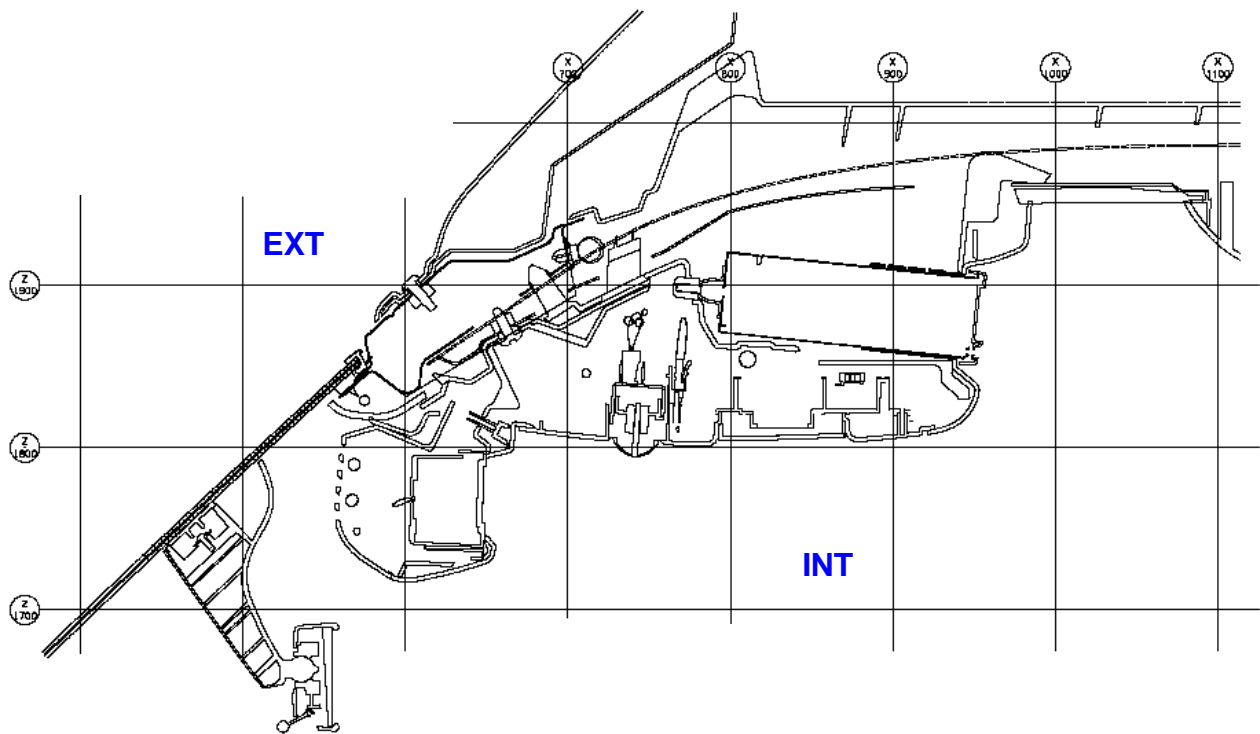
"GEDEELTE DAK - VOORRUIT"
